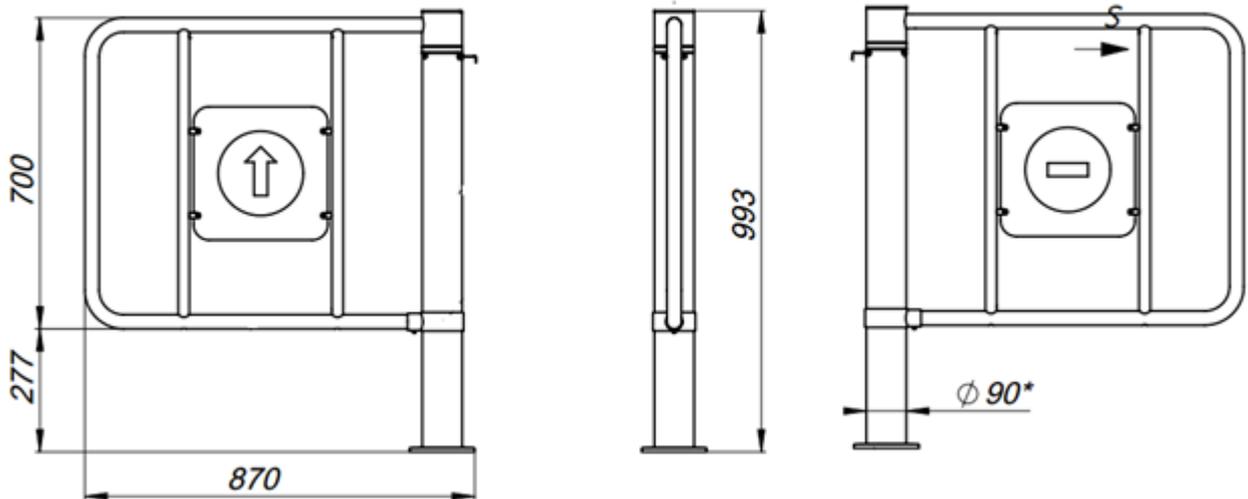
Габаритные размеры калитки размером 870 мм
